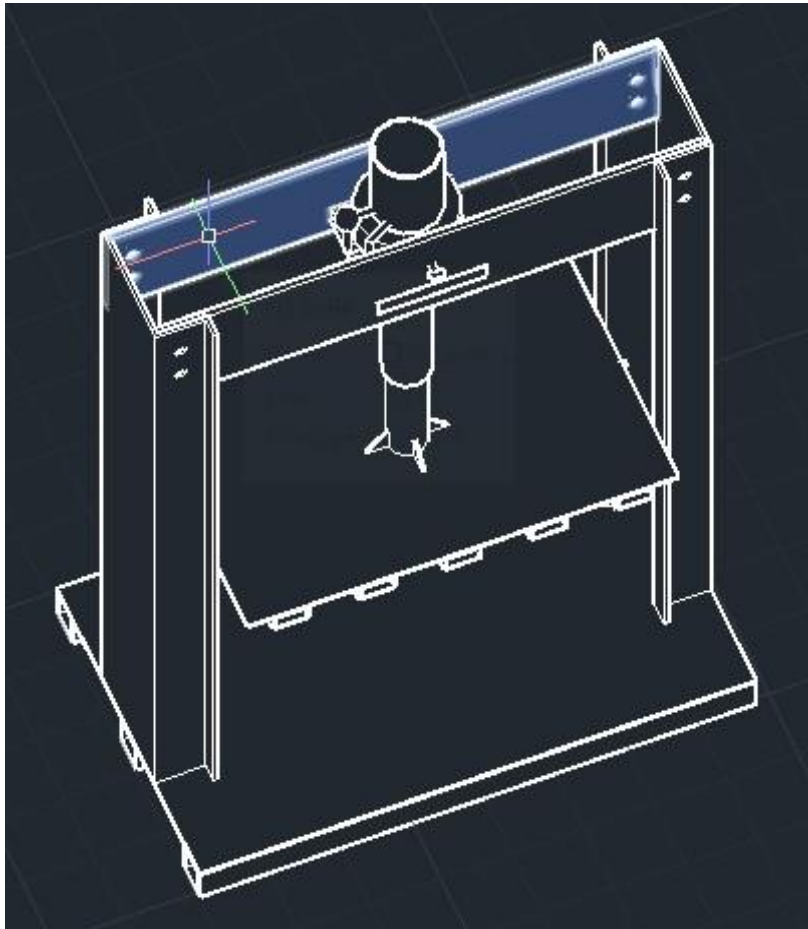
Vista en perspectiva de la prensa hidráulica sin cobertura y del travesaño posterior resaltada en azulino.
